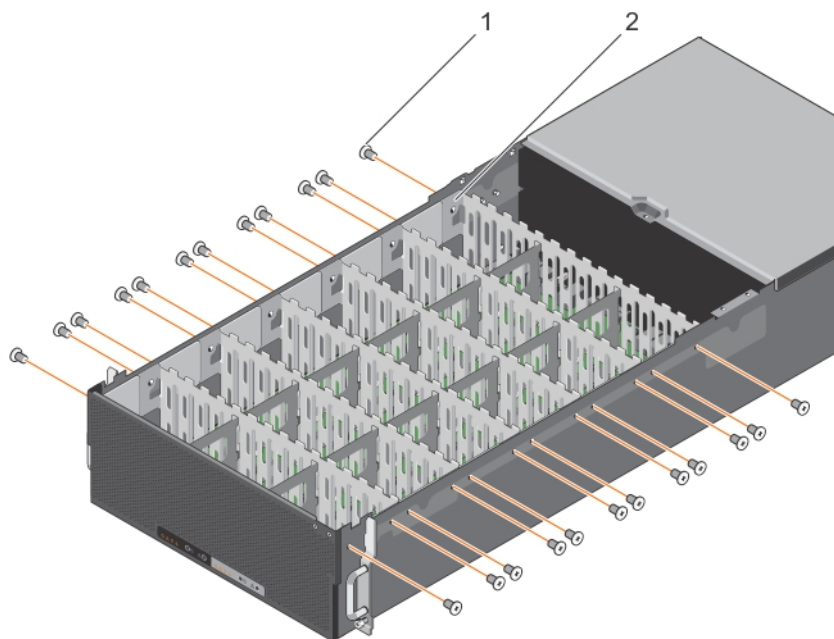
Entfernen und Installieren des Festplattengehäuses
